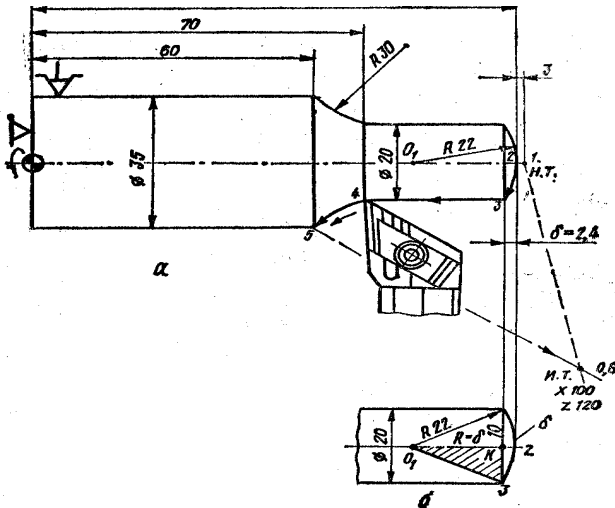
Ескіз деталі і циклограма руху інструменту при обробці деталі з двома сферичними поверхнями: а – схема деталі; б – геометрична побудова (для визначення розміру δ).
